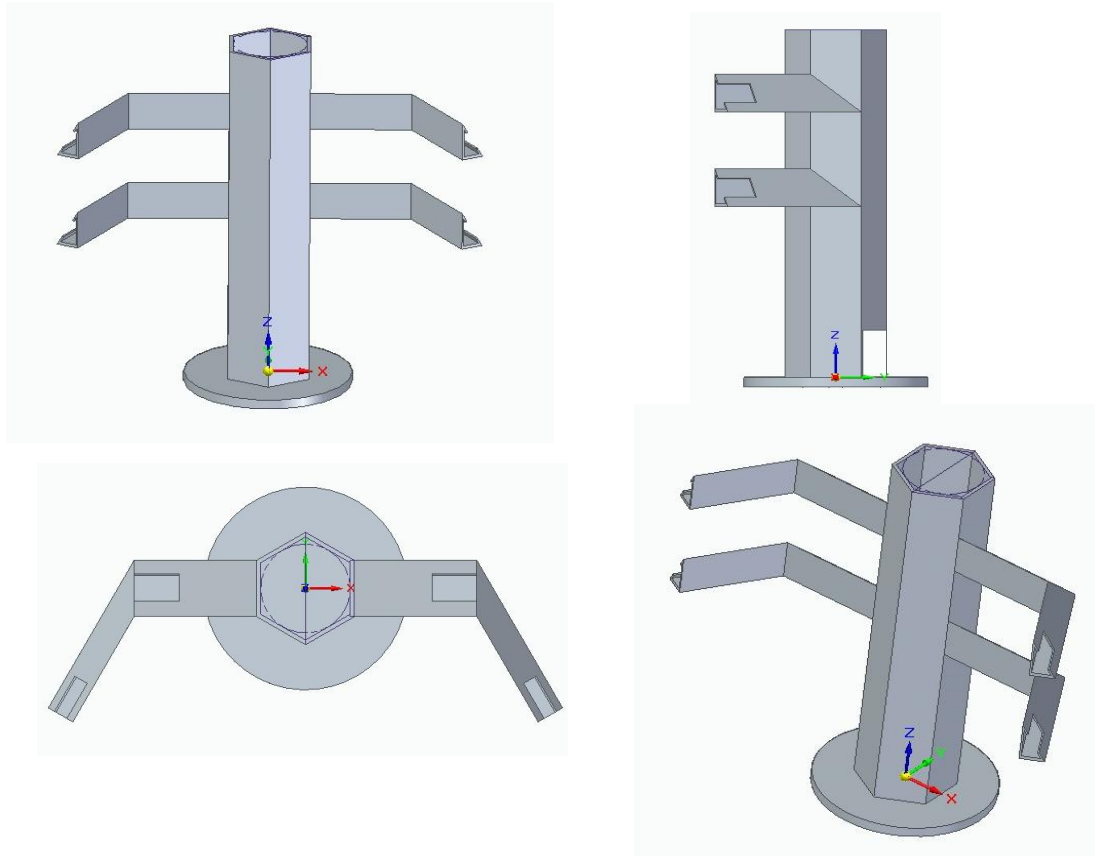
Alzado, planta, perfil y vista 3D de la versión inicial de la estructura.
